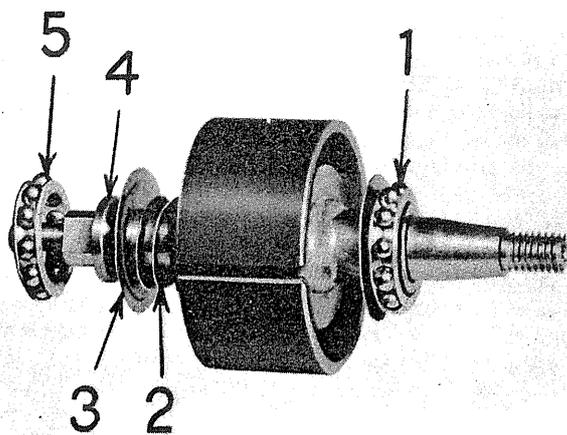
AIMANT DU ROTOR H-4 AVEC ARMATURE, ROULEMENTS, ET CALES. 1 - ROULEMENT AVANT. 2 - CALES DU ROTOR. 3 - CUVETTE DE RETENUE DE LA RONDELLE EN FEUTRE. 4 - CAGE INTERIEURE DU ROULEMENT. 5 - MANCHON DE RETENUE DU ROULEMENT AVEC BILLES.
